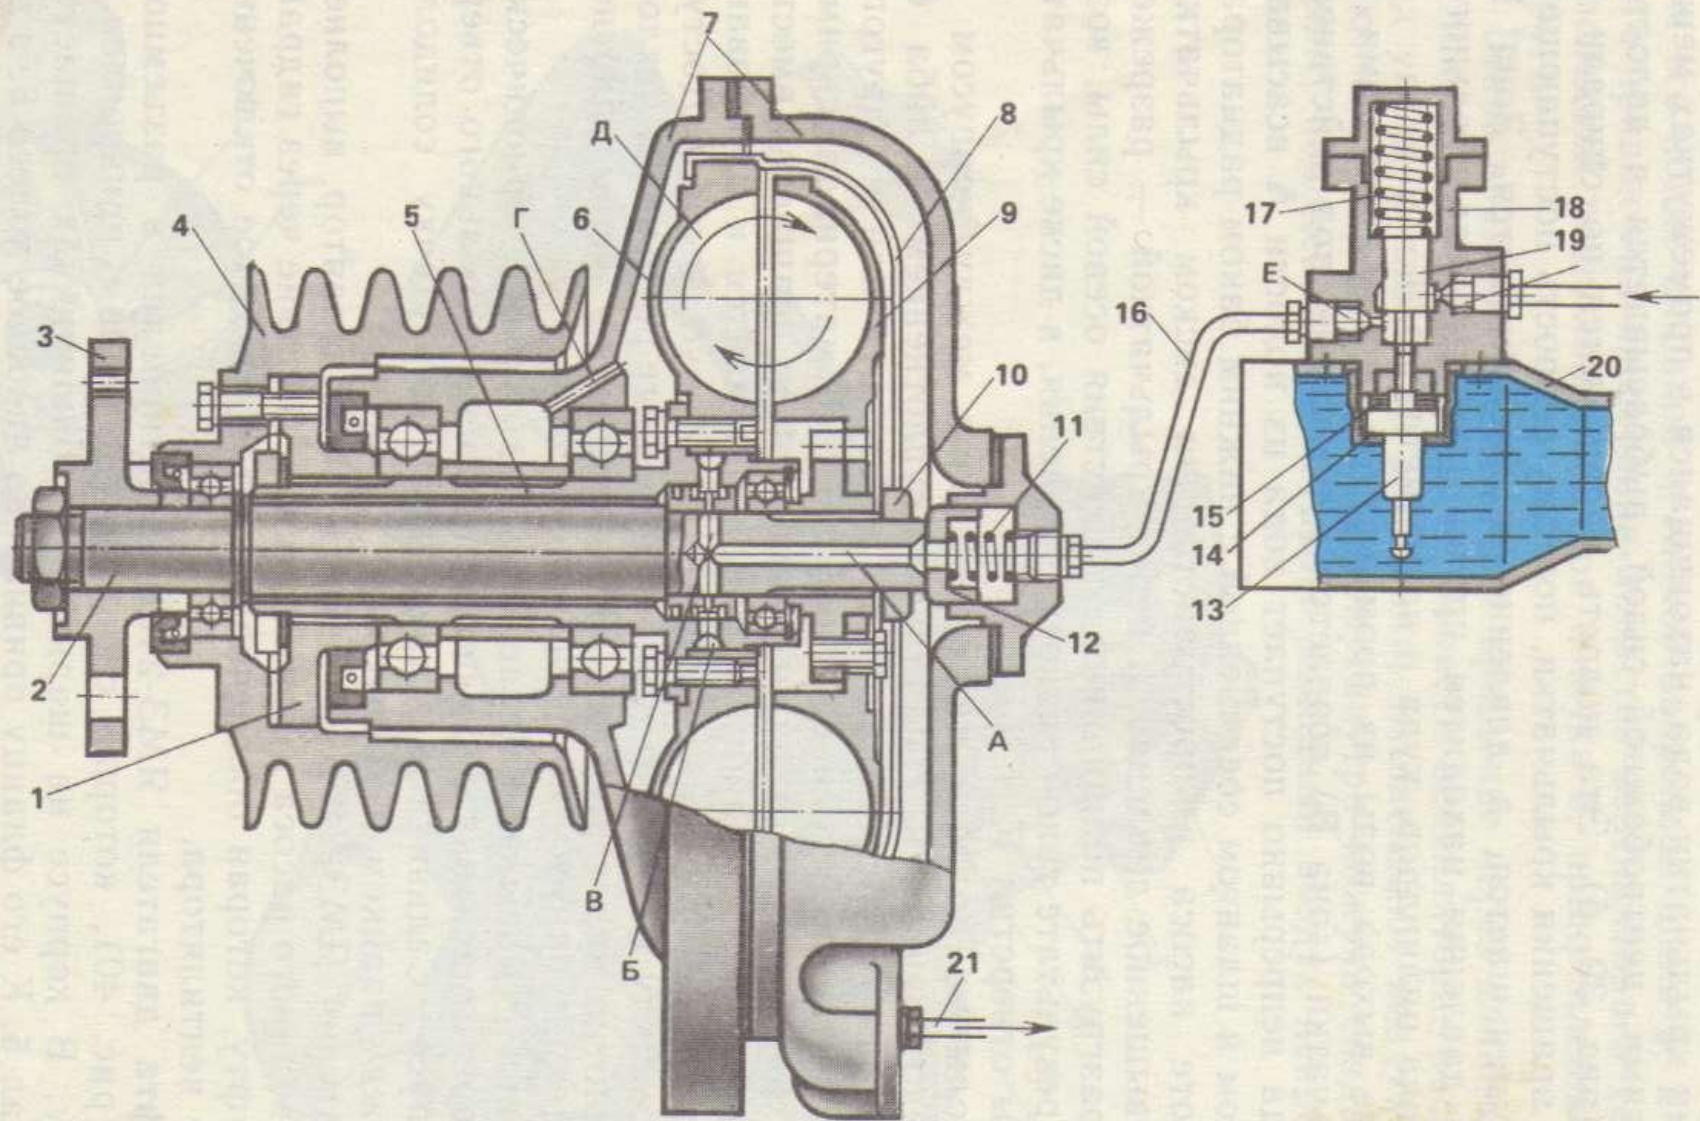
Привод вентилятора двигателя ЯМЗ-240Б:
